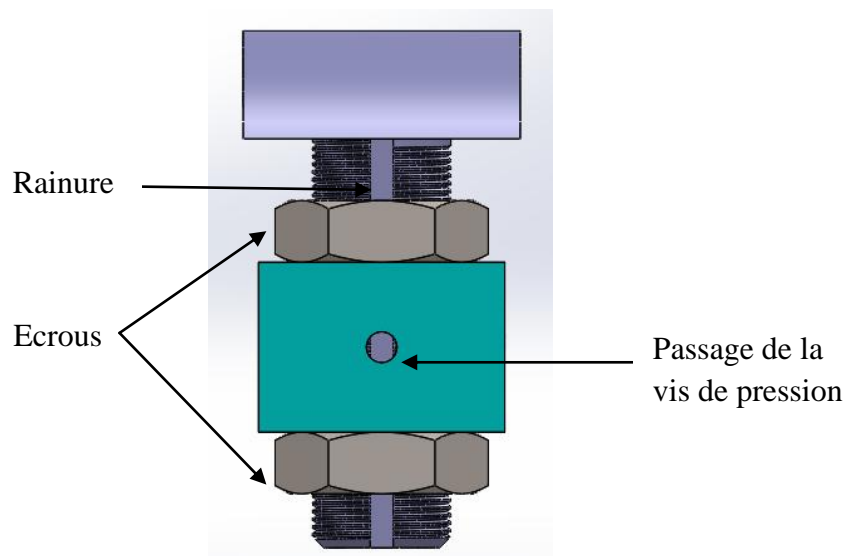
Assemblage cube-pièce fixe avec système de guidage et de fixation.
